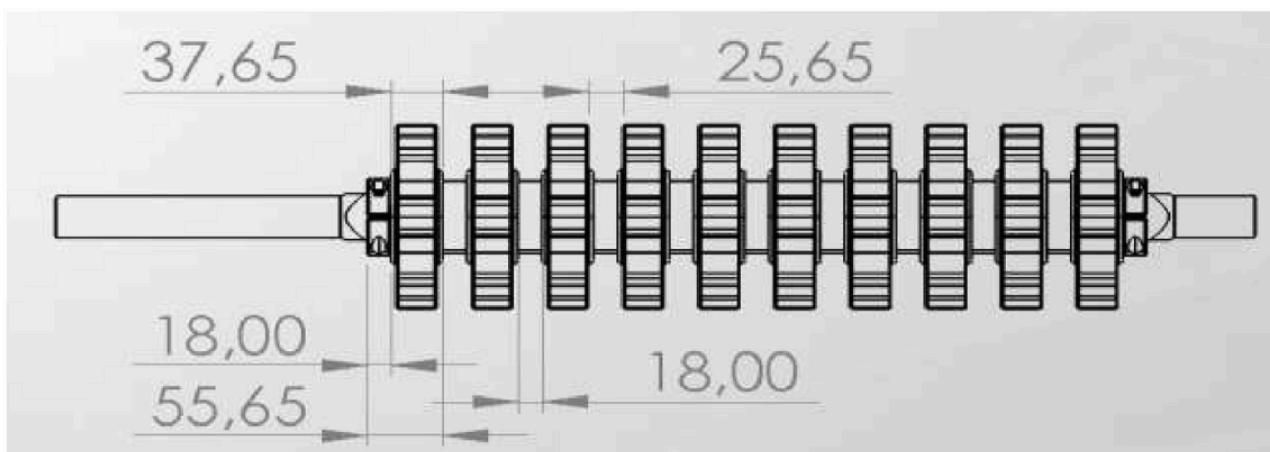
Conjunto estándar de engranajes transportadores flexdrive.
